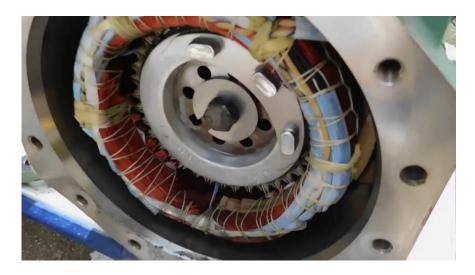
Fig. A : Vue de coté de moteur électrique du compresseur Bitzer.
